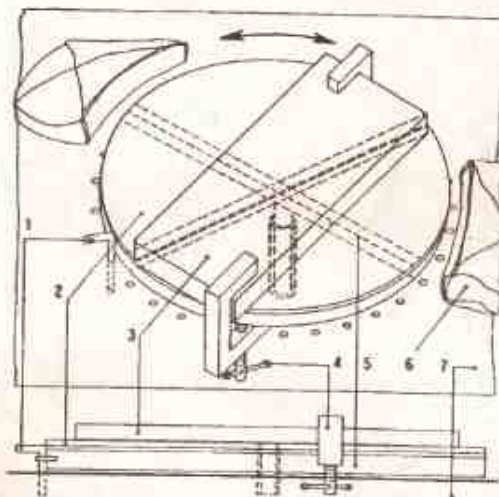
Приспособление для резьбы: 1 — фиксатор; 2 — вращающийся диск; 3 — заготовка; 4 — струбцины; 5 — ребра жесткости диска; 6 — подкладки; 7 — столешница
